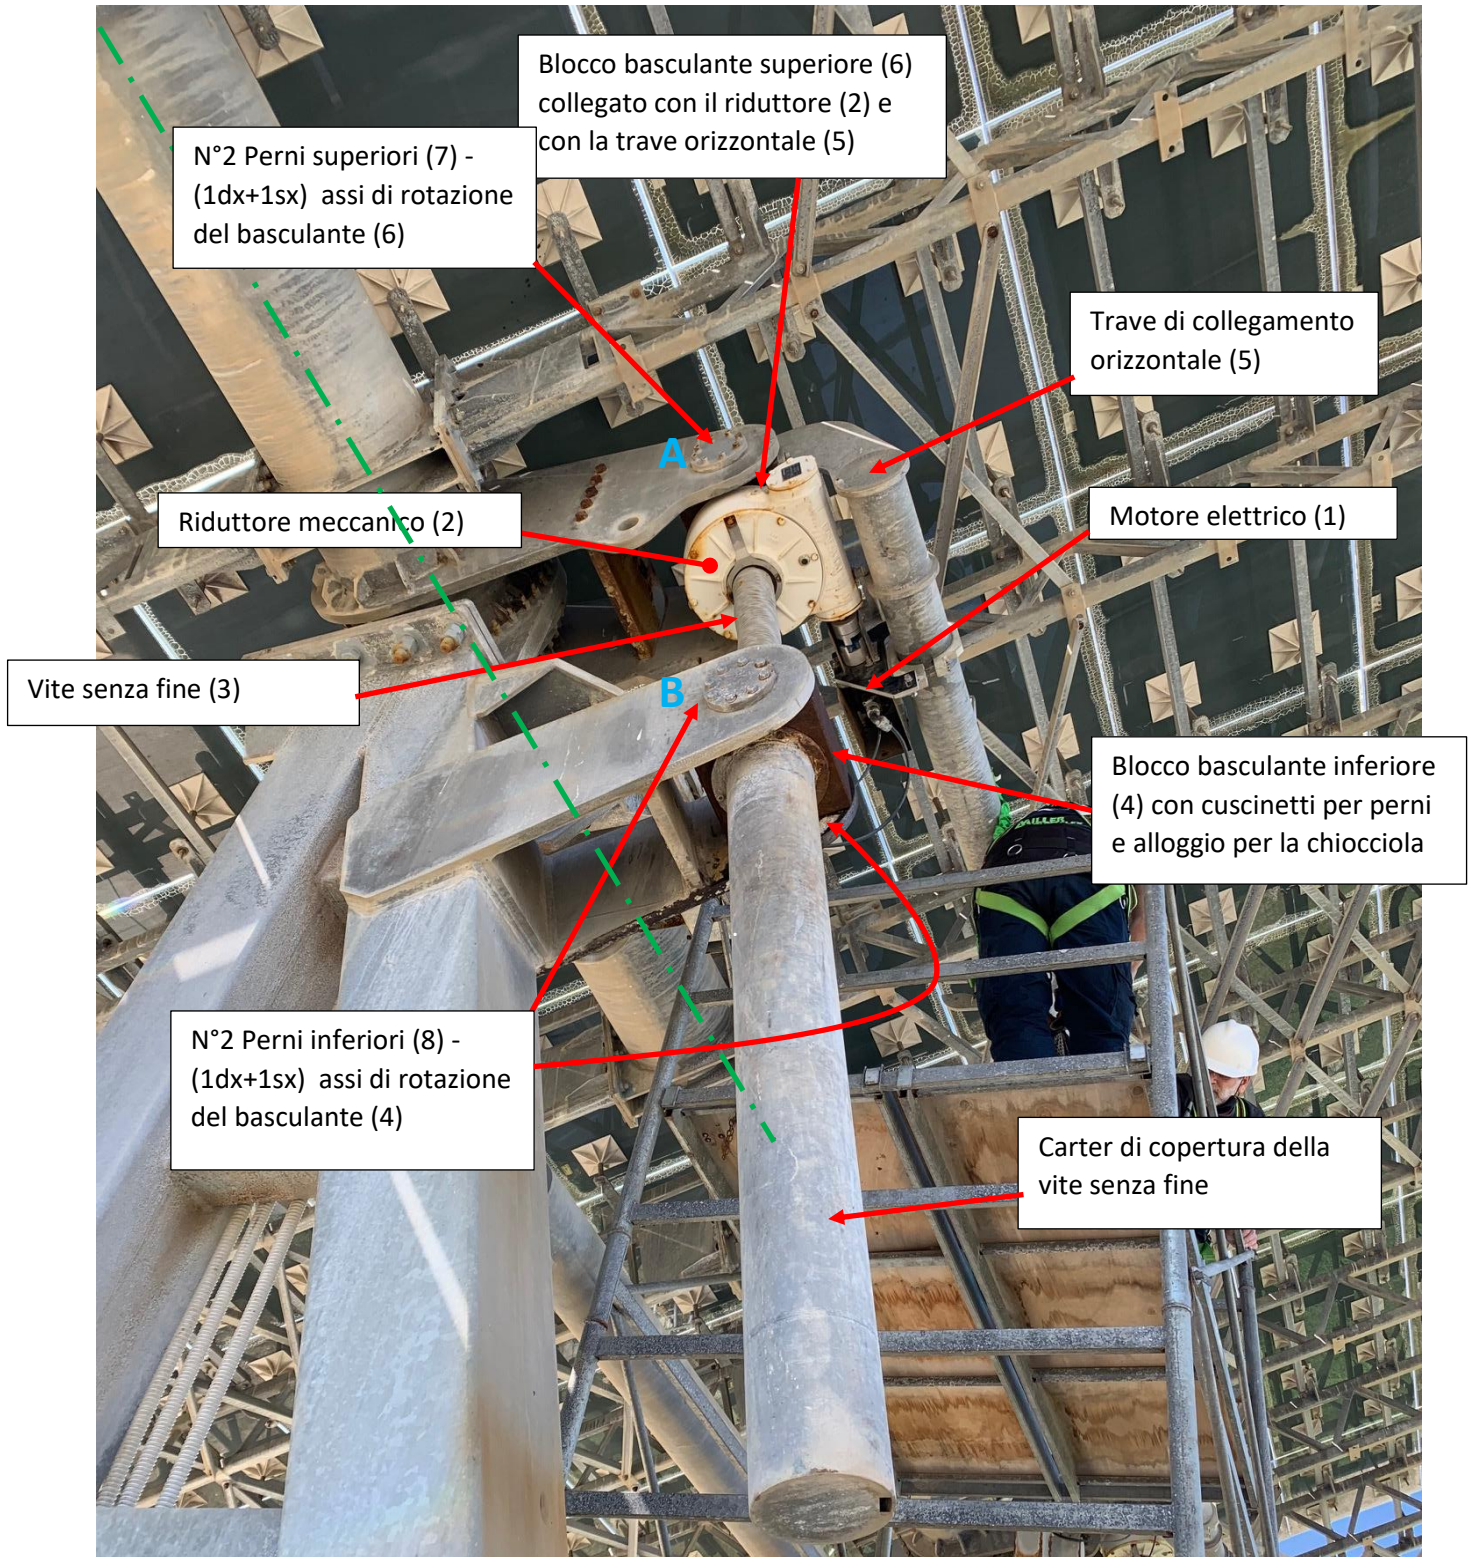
Vista del sistema di movimentazione in elevazione dell'eliostato
